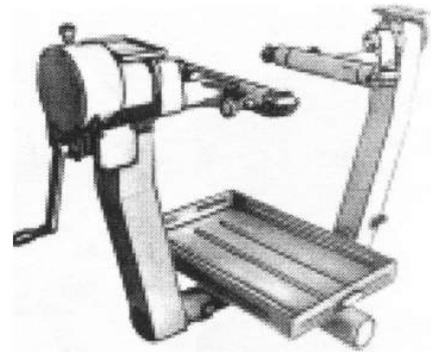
Стелд для разборки и сборки двигателей грузовых автомобилей, мод. Р 642М
